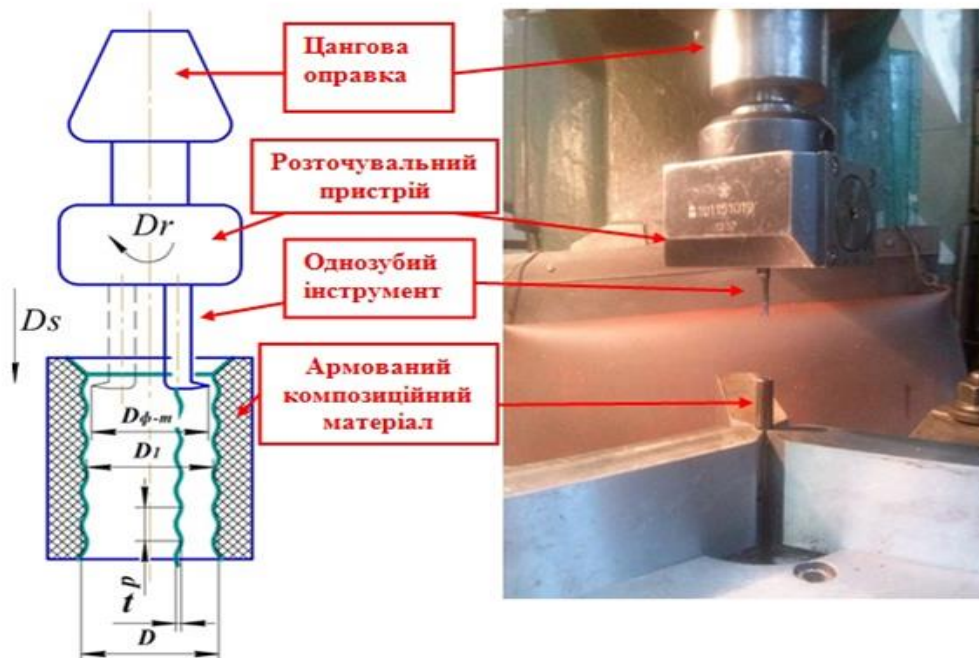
Оброблення круглої різьби в АКМ: а) спрощена схема оброблення;
